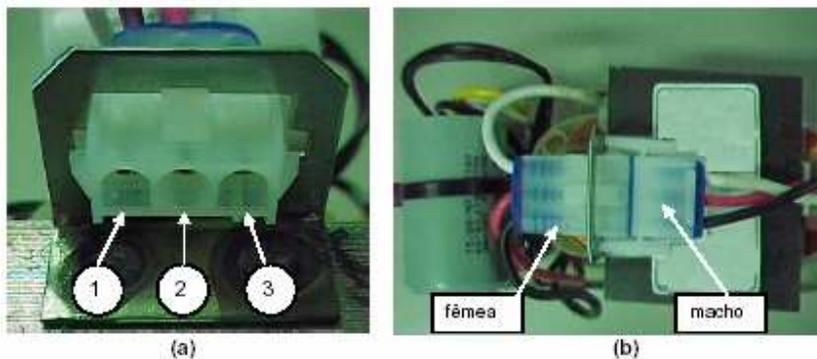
Detalhes do conector MATE-N-LOK fixado no kit removível
